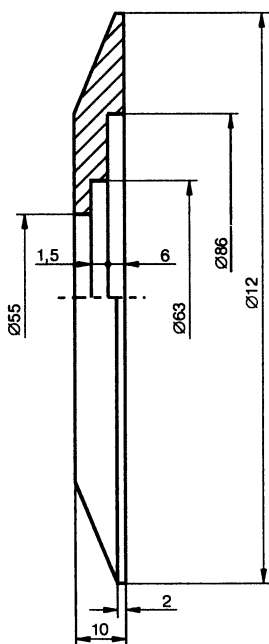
Чертеж декоративной накладки для ВЧ-головки
